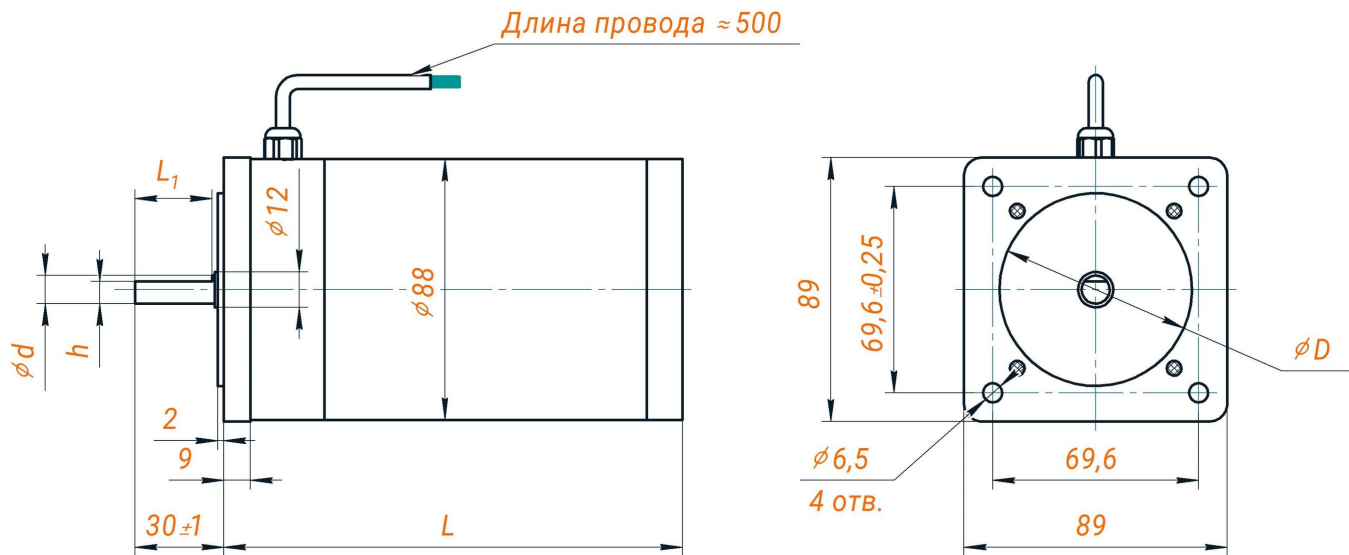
Габаритные размеры шаговых двигателей с IP68 серии 86
